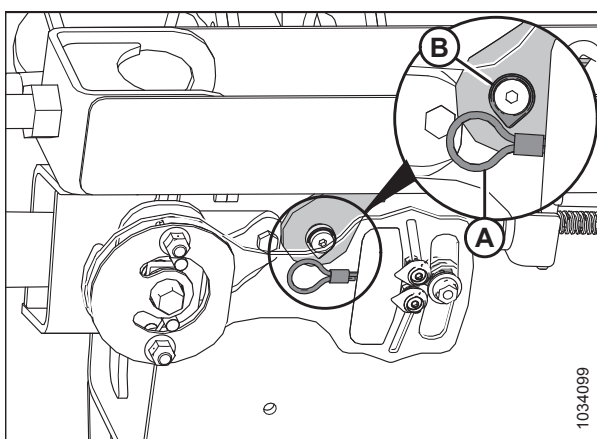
Trava do cabo Flex Checker – Esquerdo
